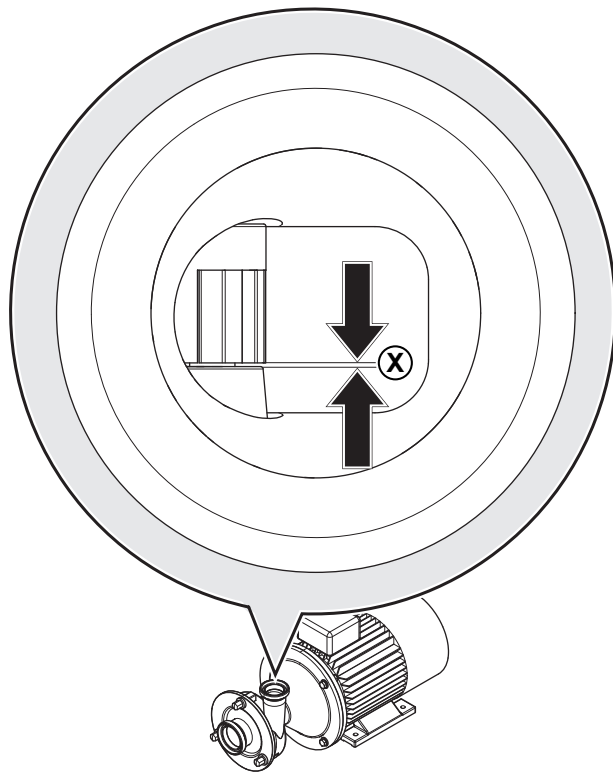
Измерение зазора "рабочее колесо - крышка корпуса"
